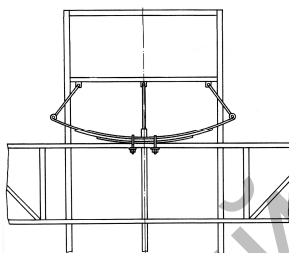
Схема маятниково-рессорной навески штанги опрыскивателя [38]
